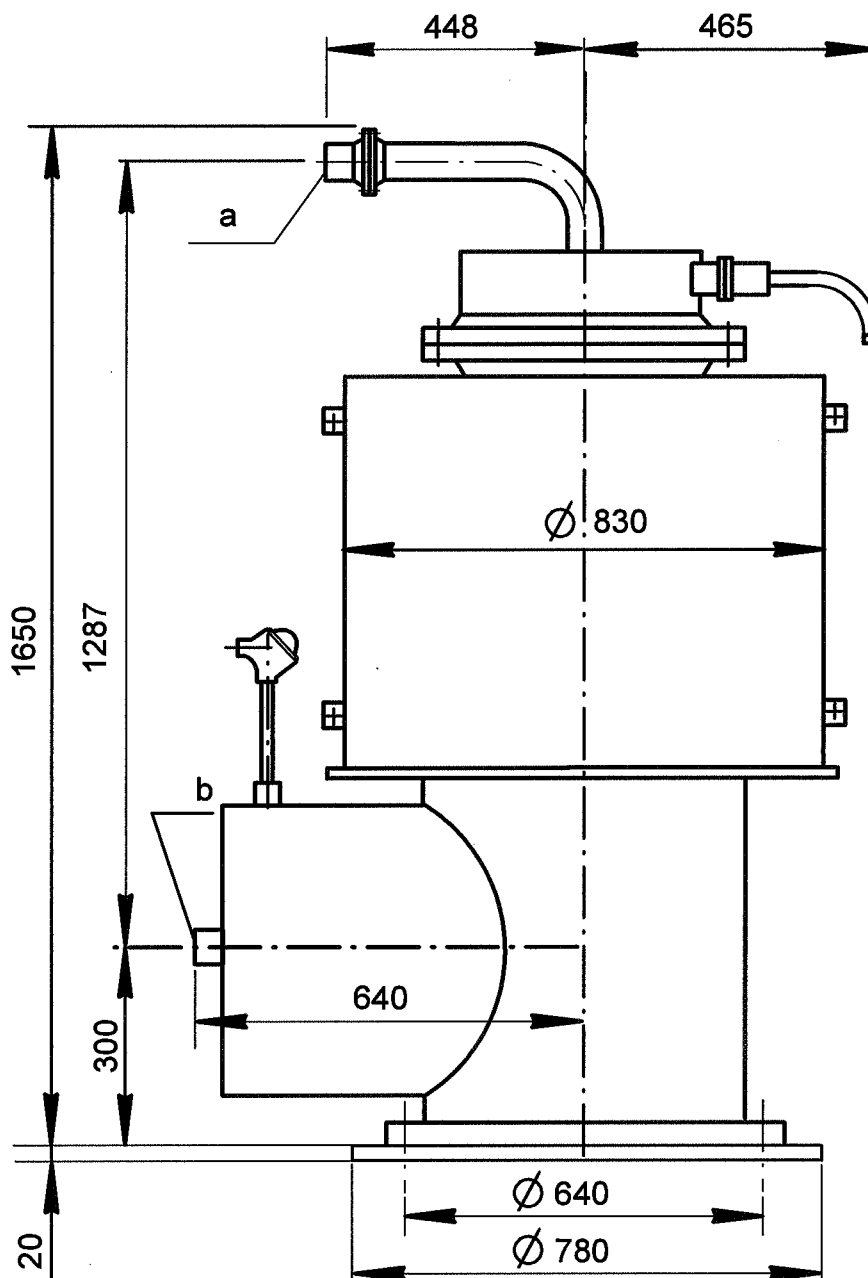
Габаритный чертеж электронагревателя KPL41AH001, KPL41AH002
